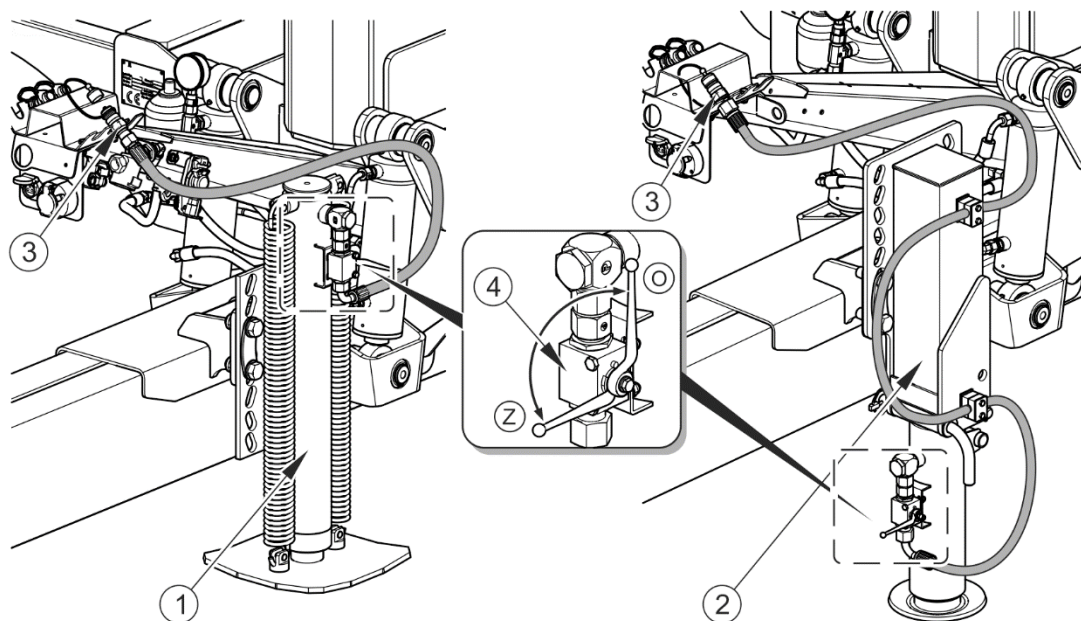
Raccordement de l'installation de la béquille hydraulique
